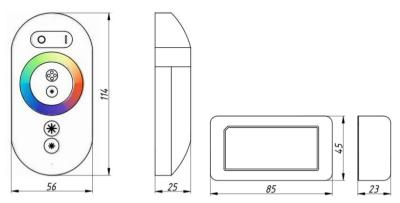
Габаритные размеры Пульт и Контроллер RGB GL-12V216WRF-S.
